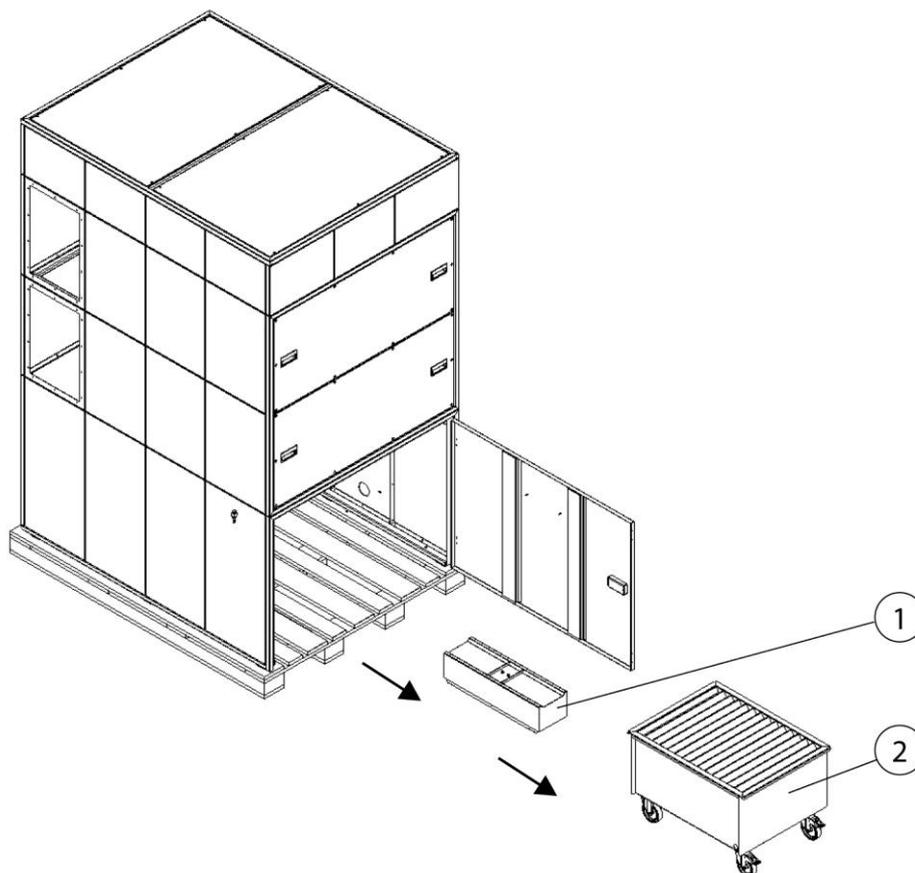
retrait du bac collecteur de poussières et du dispositif de levage
